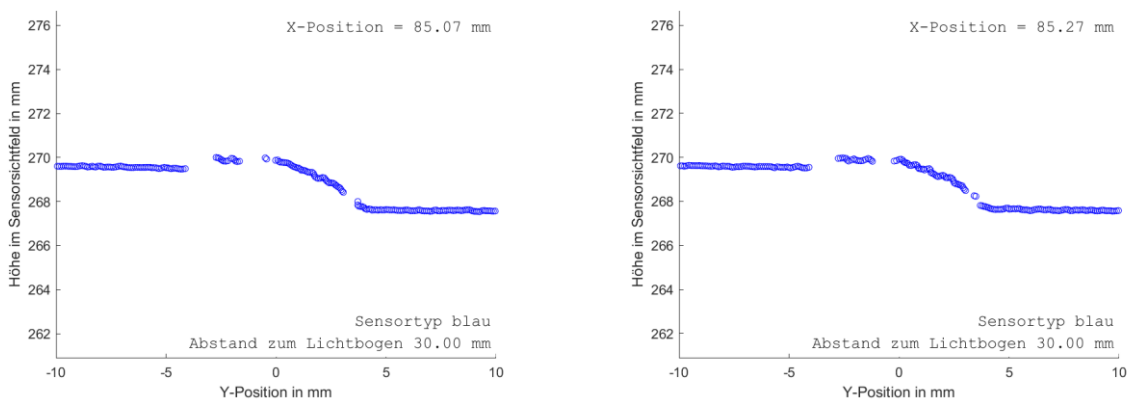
Geometrie-Profile, aufgezeichnet mit einem blauen LTS auf der glühenden Schweißnaht unmittelbar hinter dem Schweißbrenner
